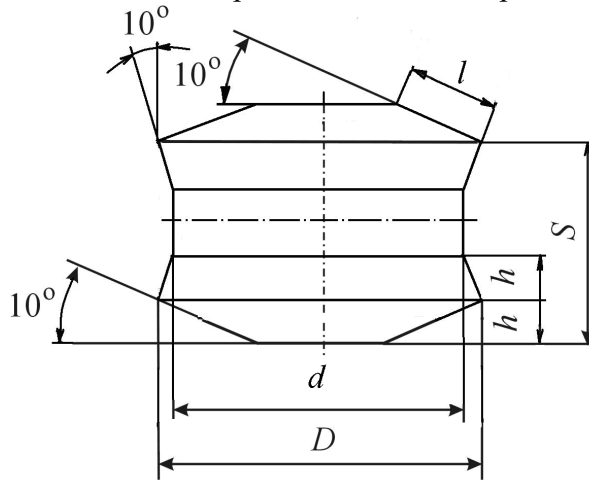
Эскиз осесимметричной режущей пластины из ПКНБ двусторонней с конической передней поверхностью
